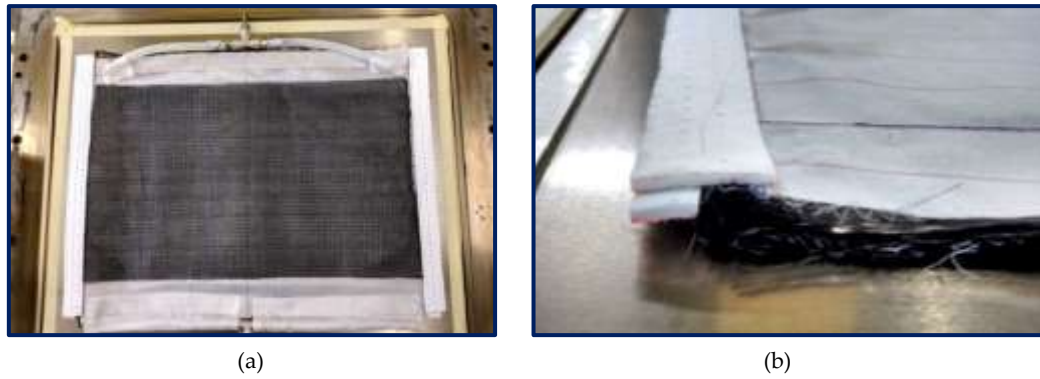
(a) Montaje de los consumibles en el molde de placa plana para la infusión del laminado M00, (b) uso de coremat a lo largo de la placa rectangular.
